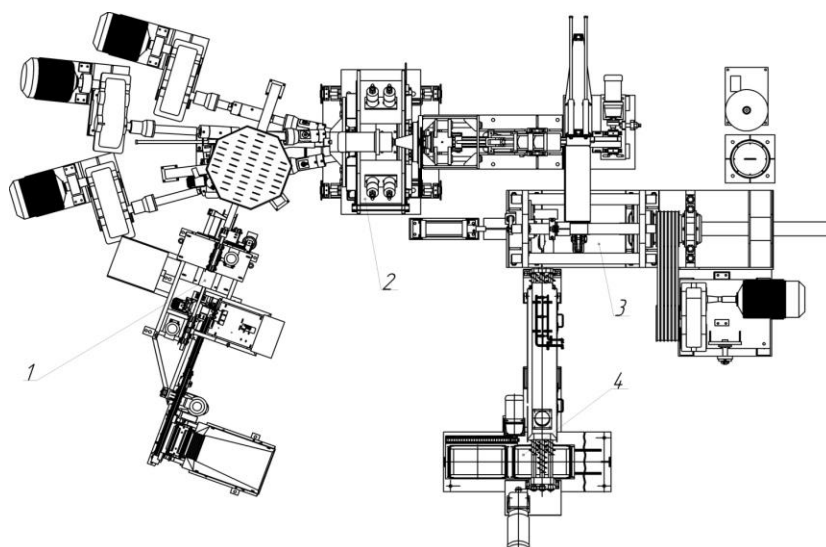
Состав основного оборудования автоматизированной линии винтовой прокатки: 1 – нагревательное устройство; 2 – трехвалковый стан винтовой прокатки; 3 - калибровочный пресс; 4 – камера контролируемого охлаждения
